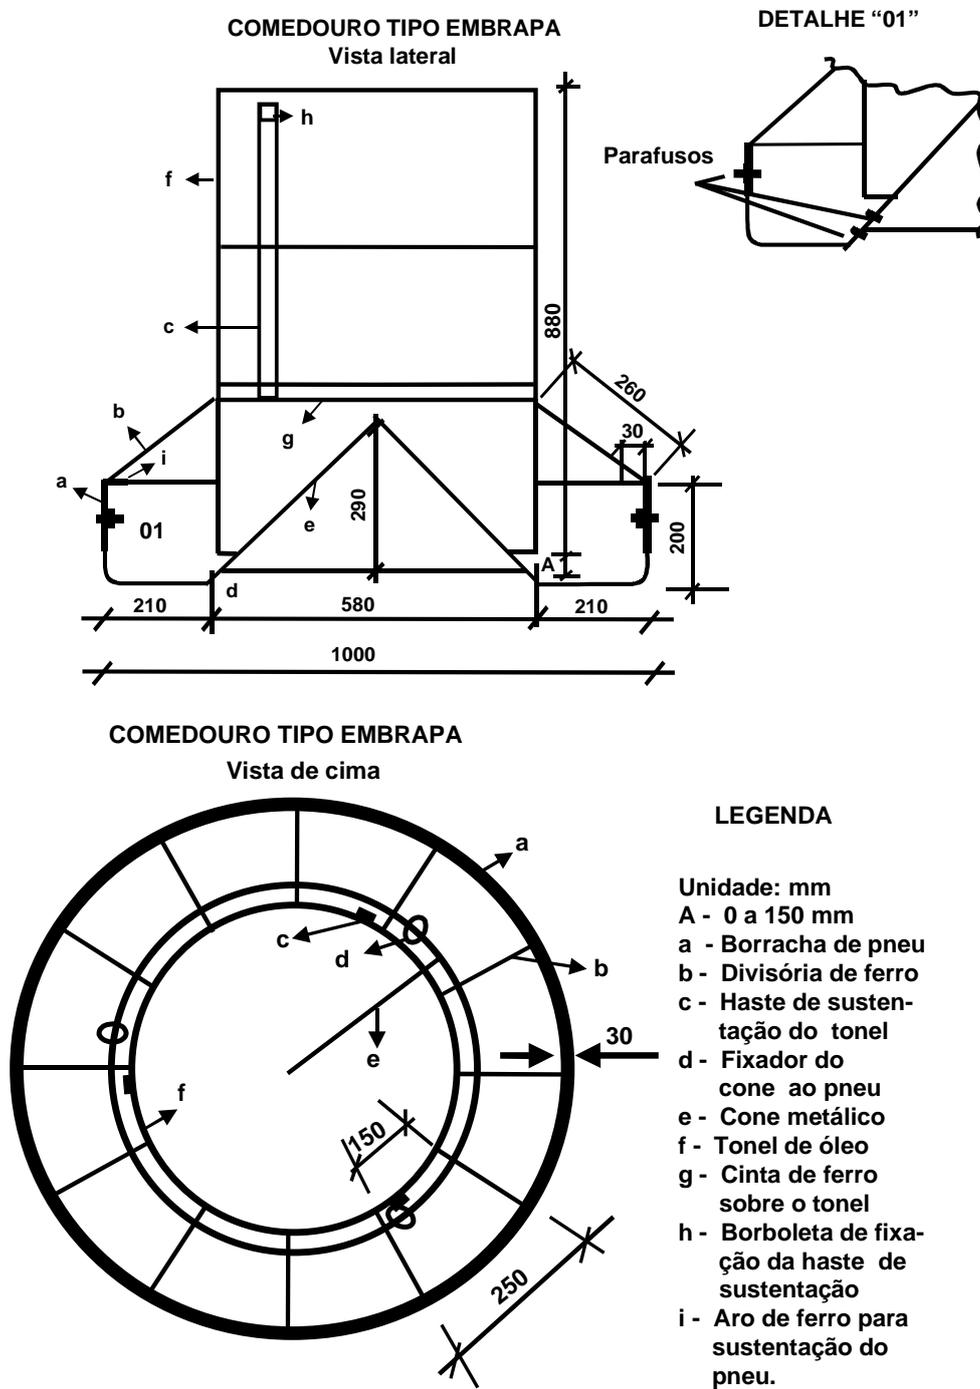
Vistas parciais do comedouro tipo EMBRAPA
